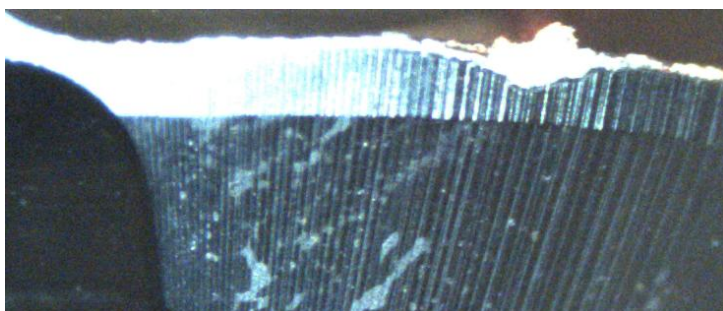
Nástroj 2 po 14 a 36 minutách obrábění
